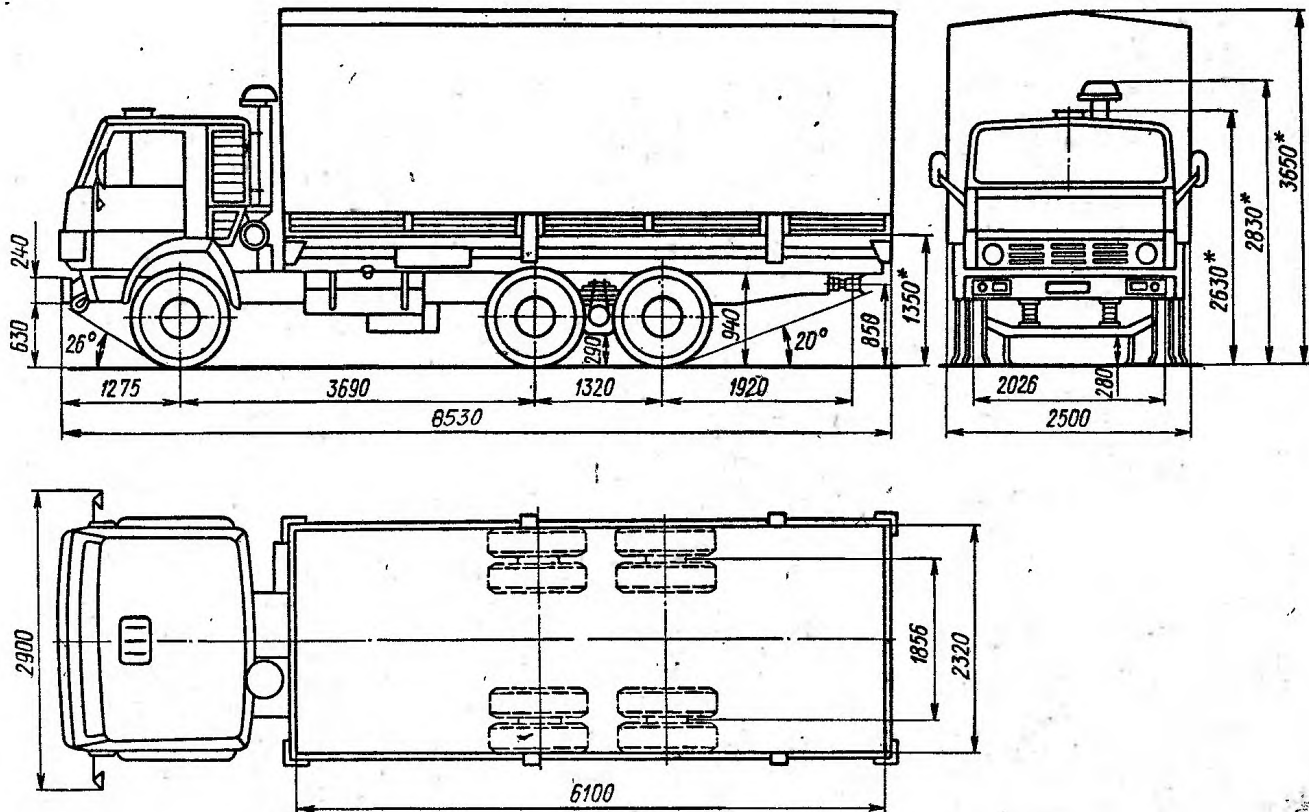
Габаритные размеры автомобиля КамАЗ-53212
